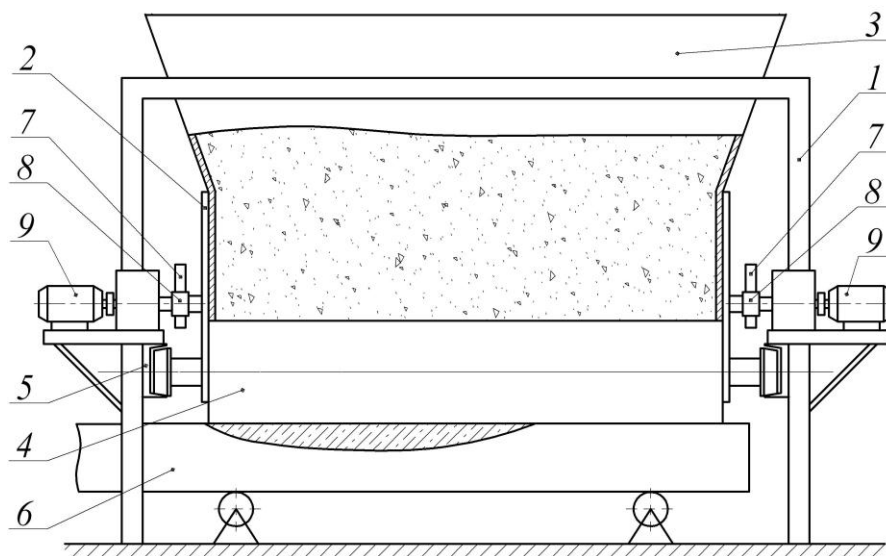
Роликова формувальна установка з двома кулачковими приводними механізмами
